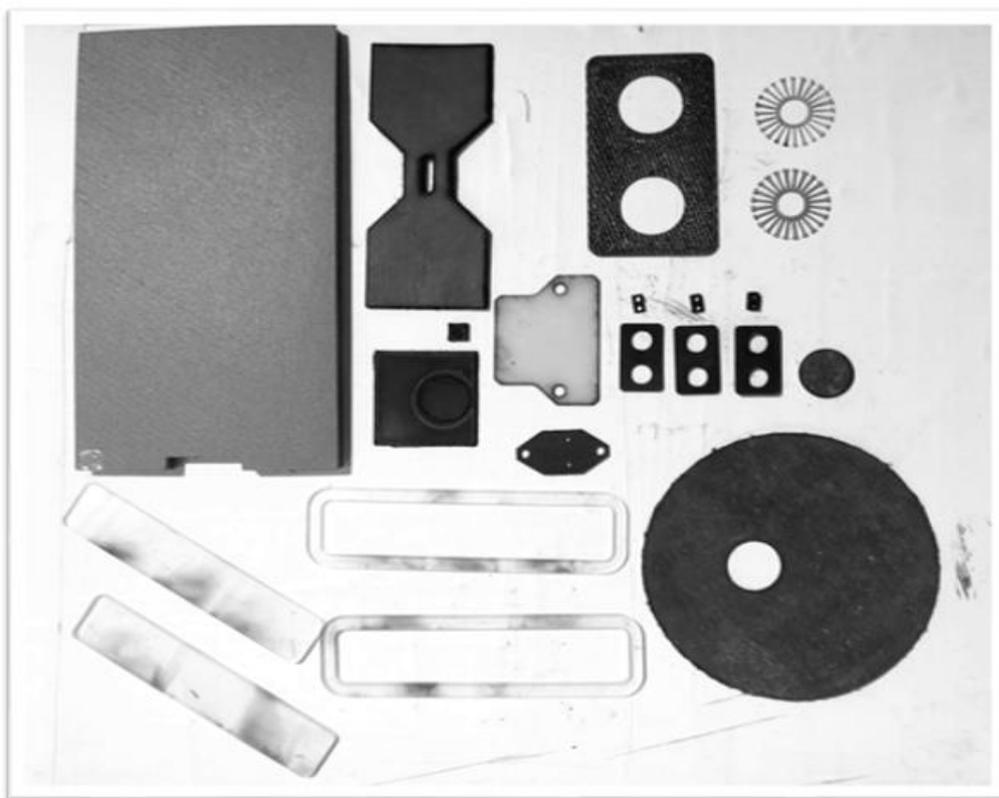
Примеры деталей изготовленных на лазерном станке
